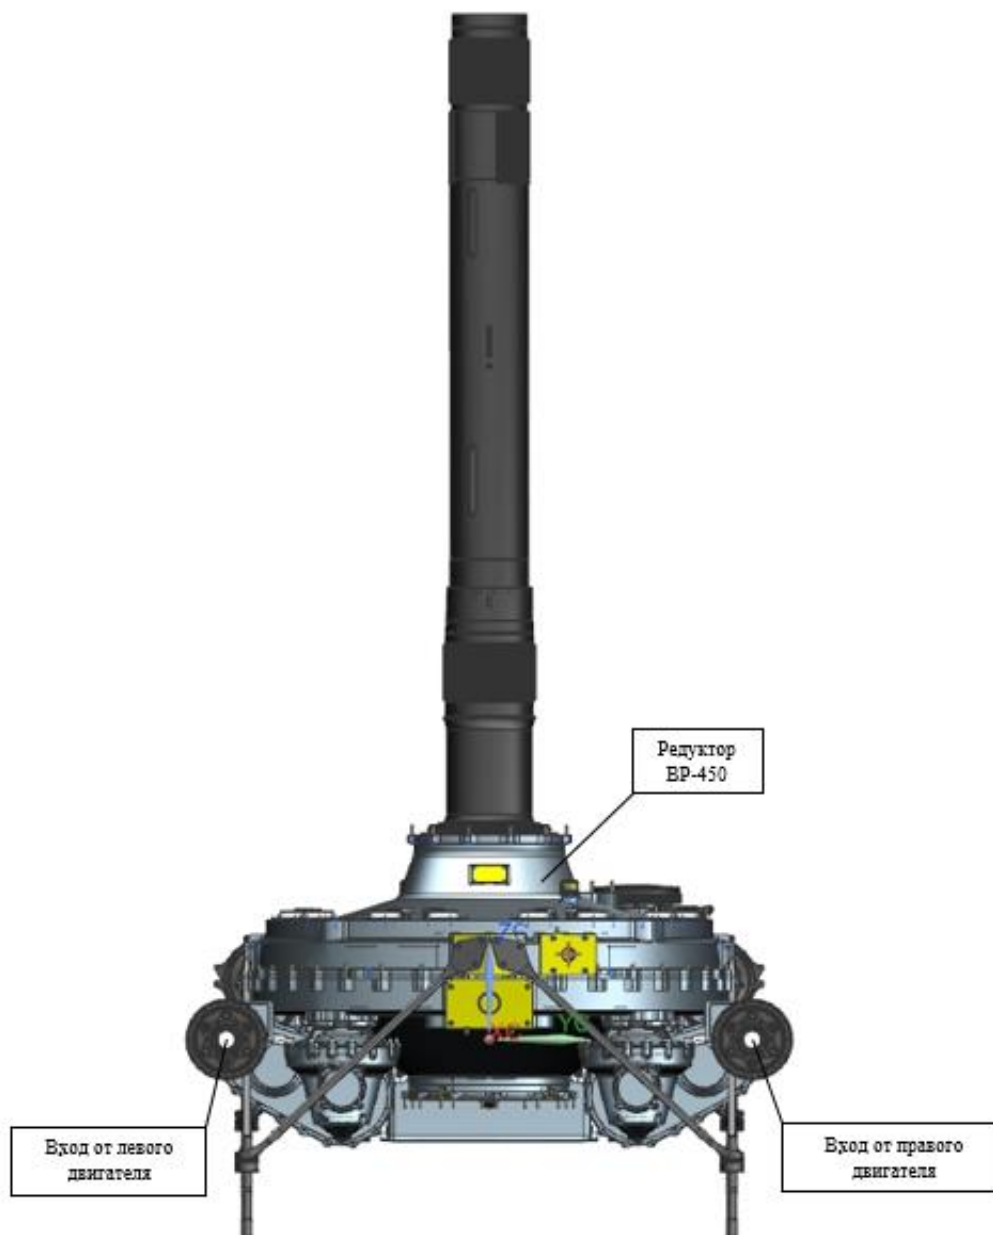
Главный редуктор ВР-450, вид спереди
